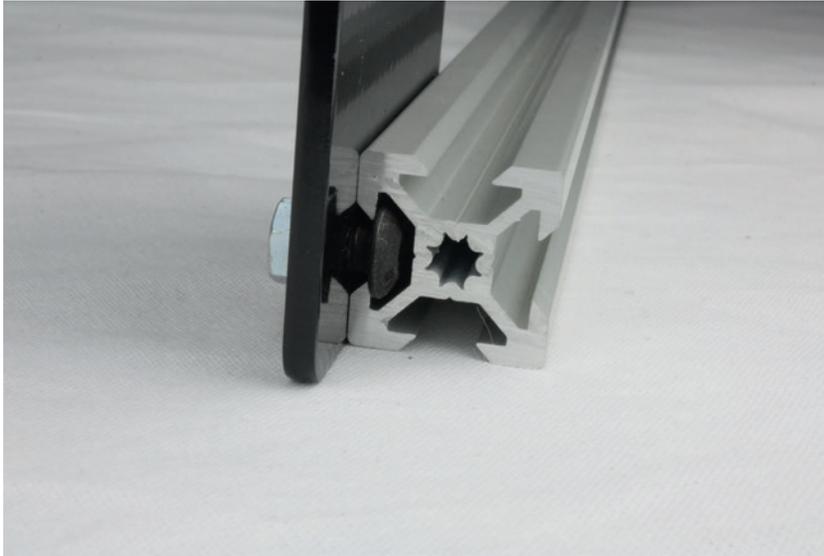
Die M5x10-Schrauben werden am Rahmen als Nutschrauben verwendet.
